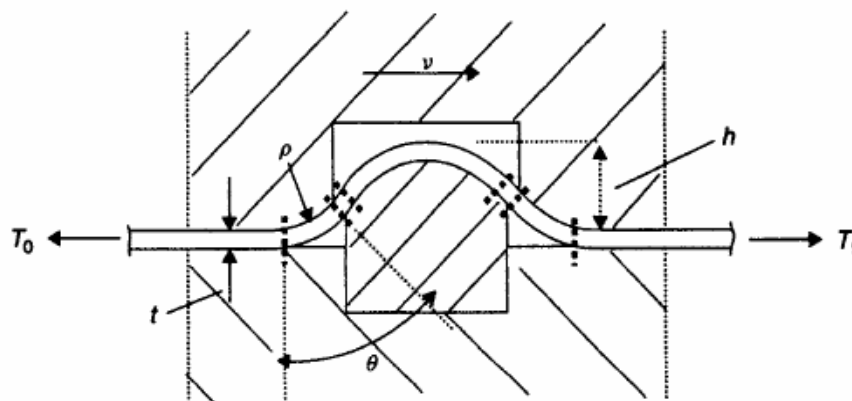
Efecto del drawbead en la tensión de la chapa
